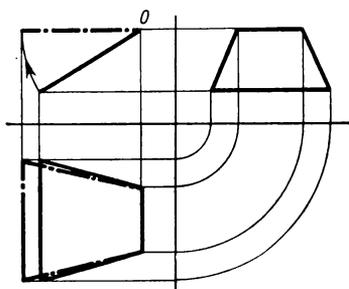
Konstruktion der wahren Größe einer Trapezfläche
